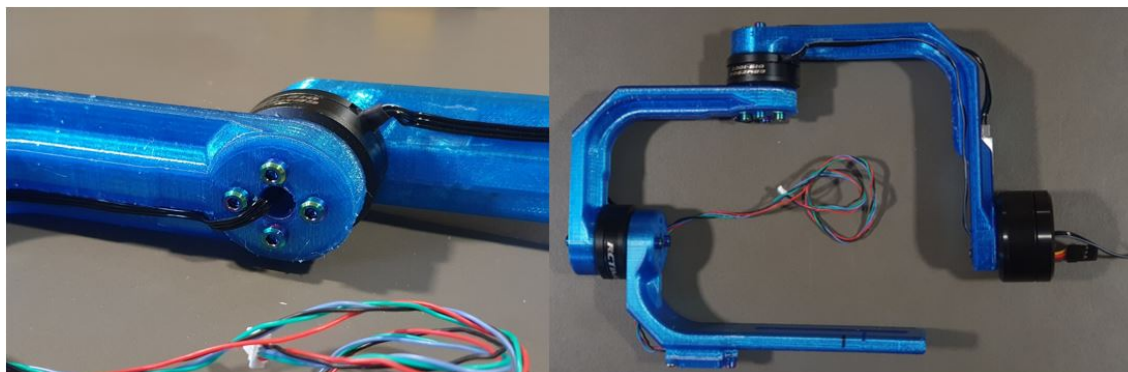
Vistes del muntatge dels motors i pas dels cables.
